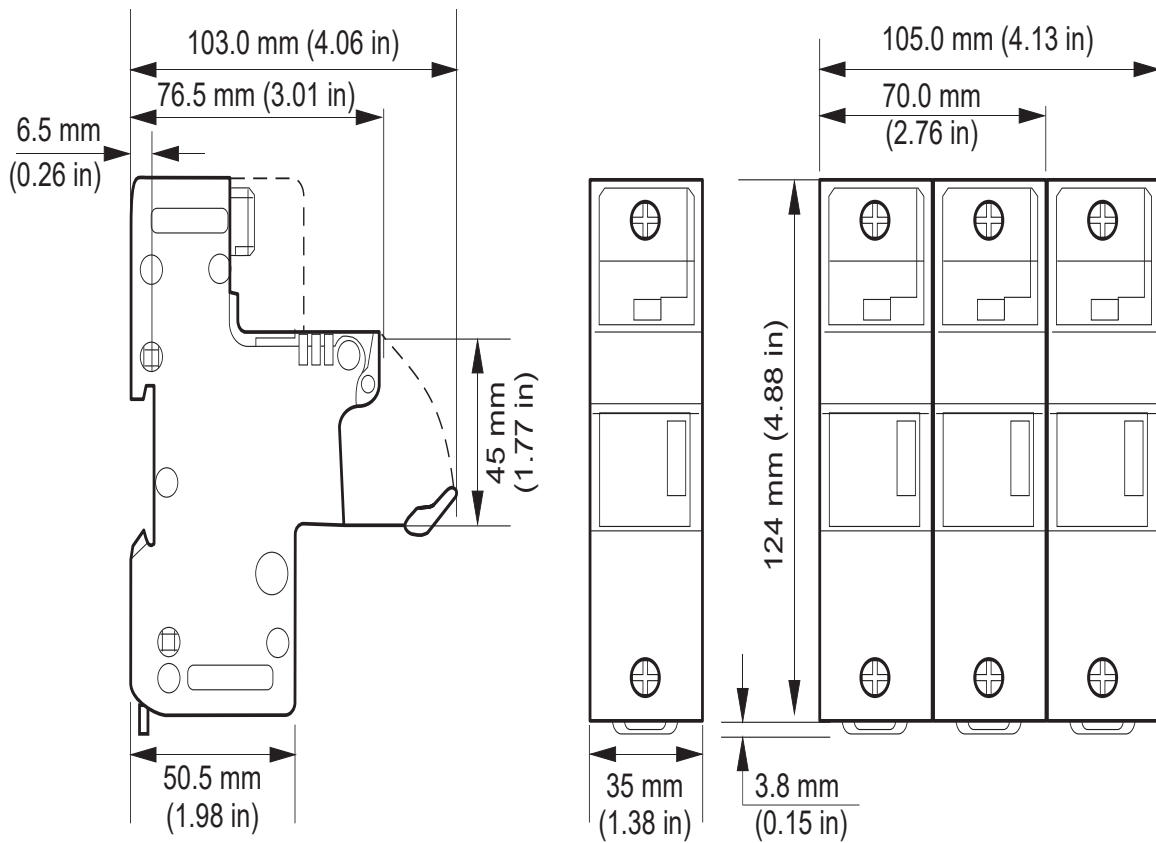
Las dimensiones del portafusibles: US221 (22x58 mm)
